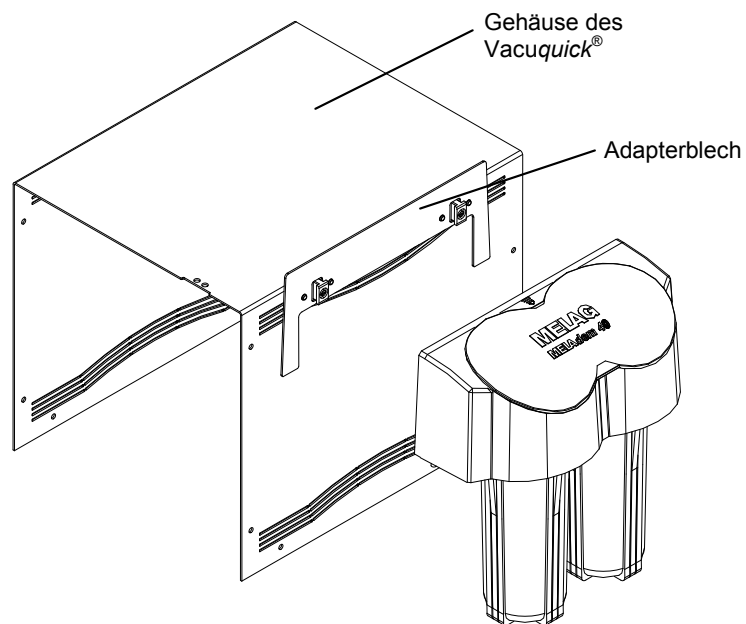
Seitenansicht – Gerätehaube des Vacuquick[®] mit Adapterblech
